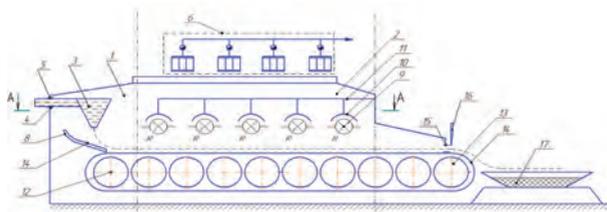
Установка конвейерной радиационной сушки биополимерного съедобного геля
